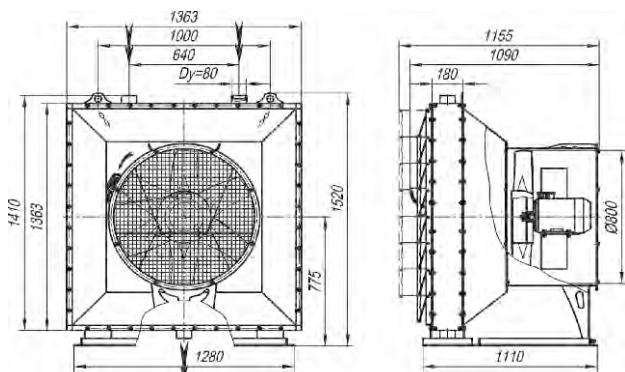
Габаритные и присоединительные размеры агрегата СТД-300П на базе парового воздухонагревателя типа КП.
